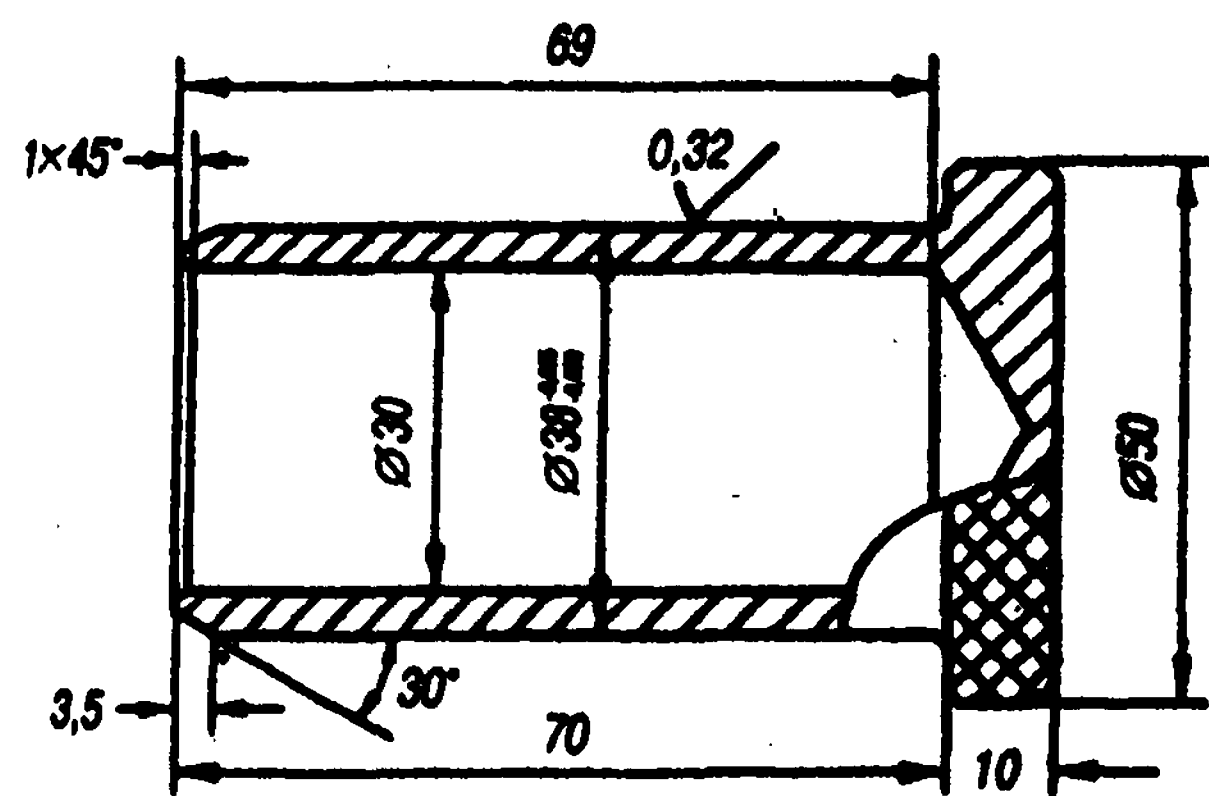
Пробка-заглушка отверстия в удлинителе коробки передач
